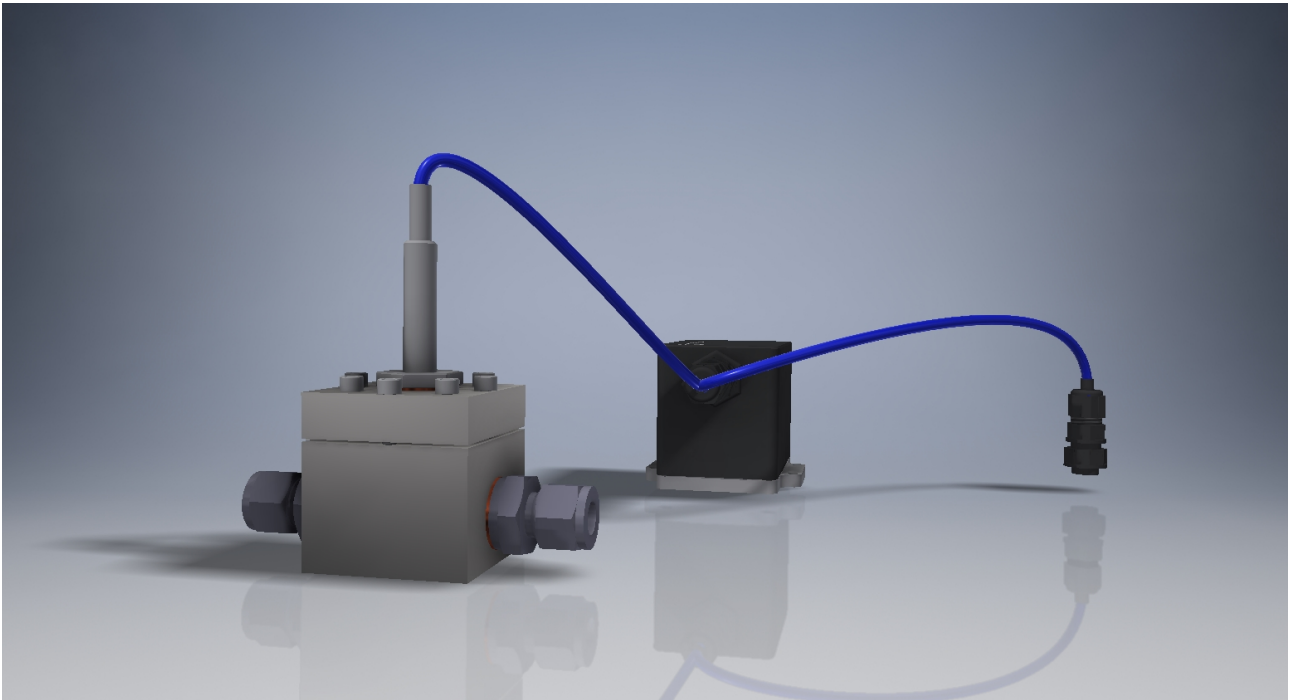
Beispiel Montage O₂-Sensorsystem mit Gehäuse für Rohranschlüsse
